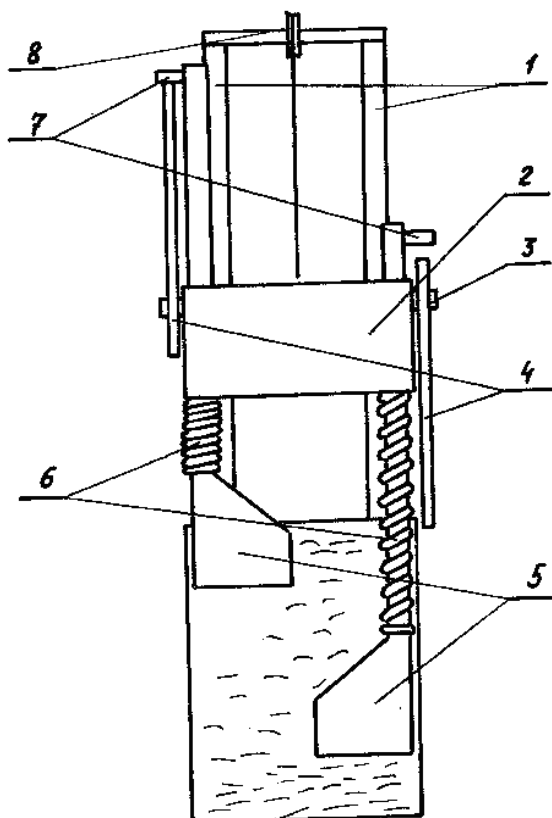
Схема уплотнителя травяной массы в контейнере: 1 – опора; 2 – приводной механизм; 3 – кулачки; 4 – вал; 5 – уплотняющие грузы; 6 – пружины; 7 – пальцы; 8 – подъемный механизм
